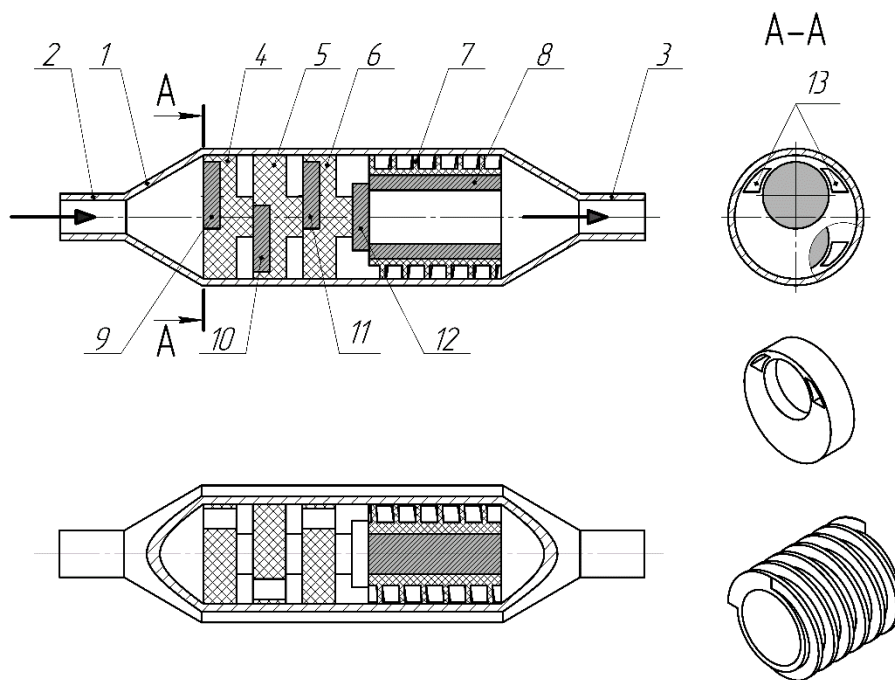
Загальний вигляд пристрою для магнітної обробки палива.
